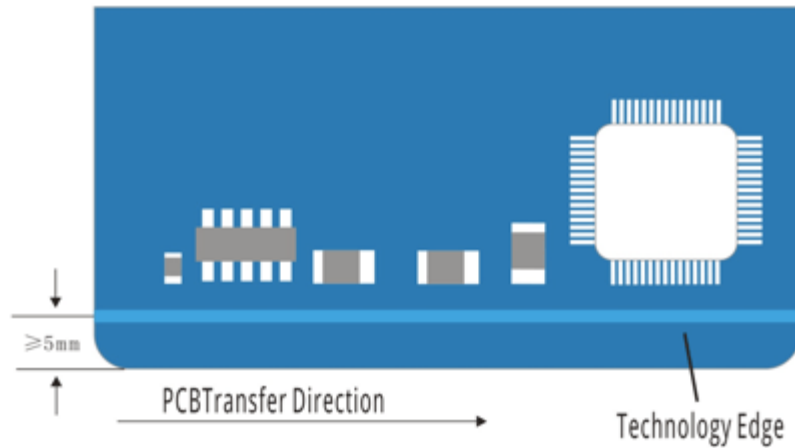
Вимога до проектування 1 PCB Technology Edge
